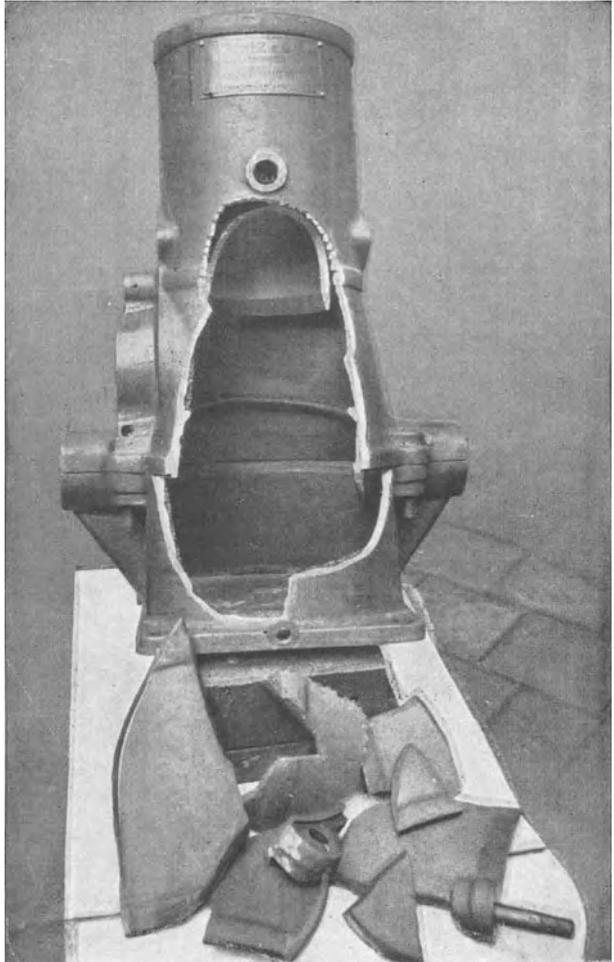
Stark beschädigter Benzinmotor vor der Schweißung.
